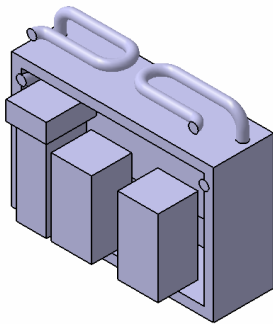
Geometría simplificada del sistema de refrigeración con heat pipes
